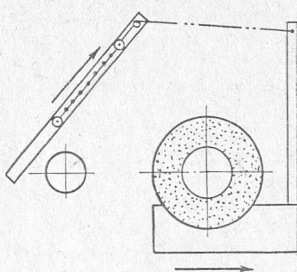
и 34. Защитное автоматическое устройство для круглошлифовального станка.
